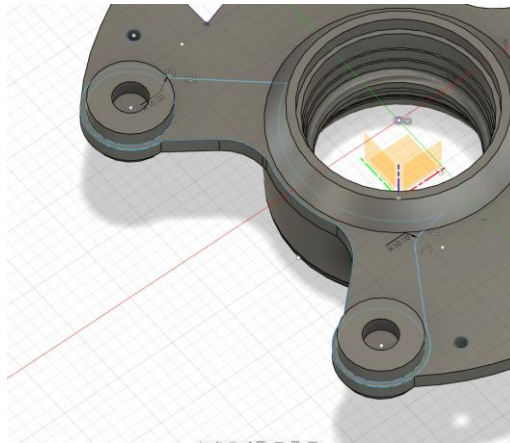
Modelado CAD – Boceto Brazos de la Pinza de Frenos (Elaboración Propia)
